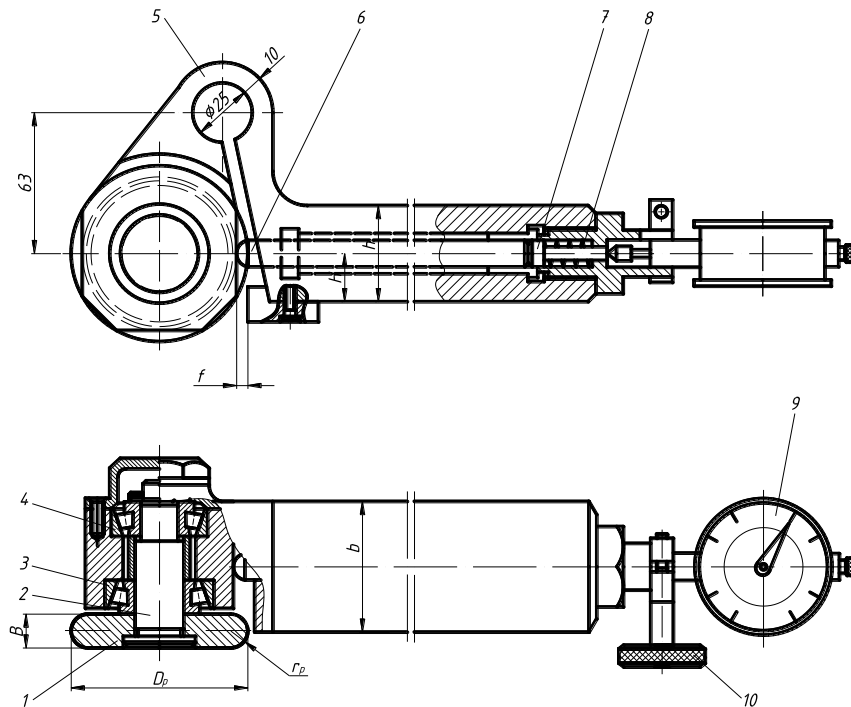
Пристрій з пружним корпусом і індикатором вимірювання зусилля обкатування:
